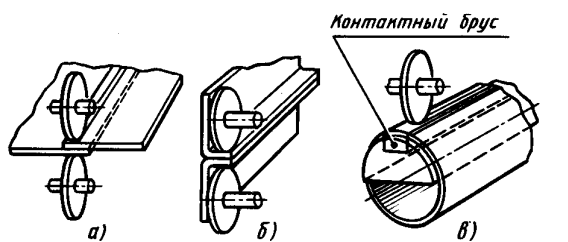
Типы сварных соединений, применяемые при шовной сварке
